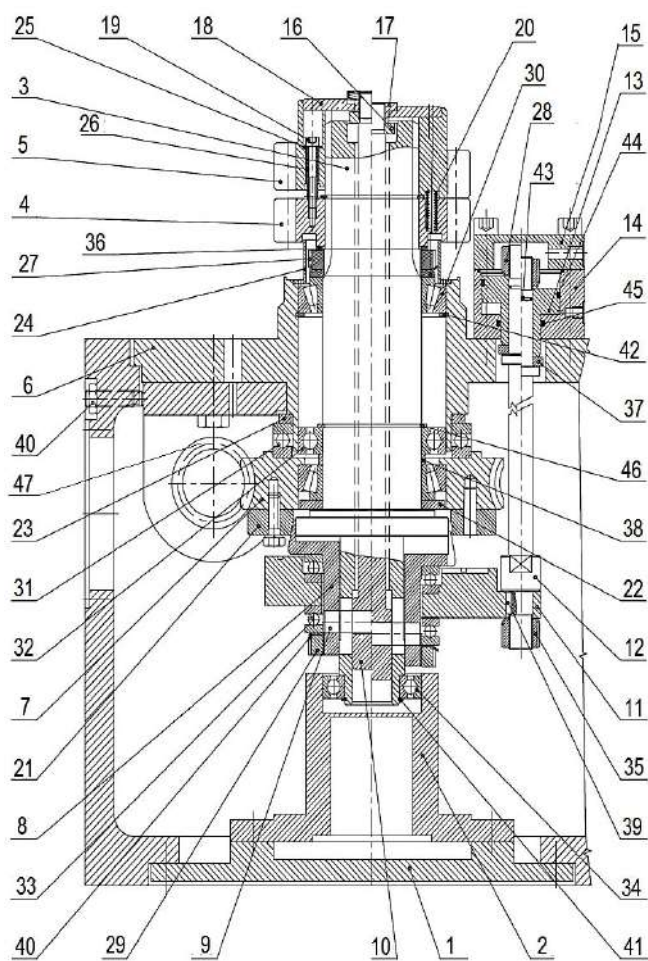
Механізм обертання планшайби (вісь С)
